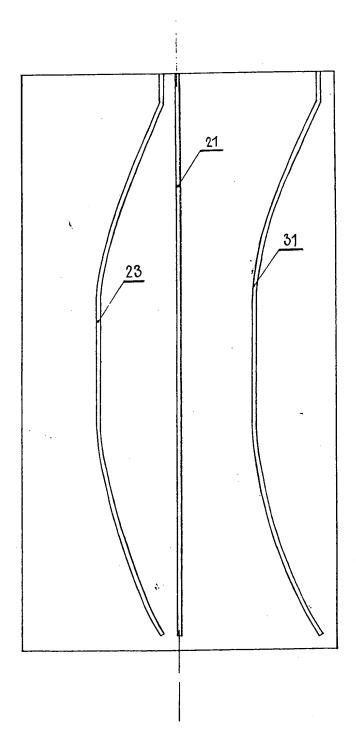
Развертка внутренней поверхности детали (1) устройства, изображенного на фиг.1.
